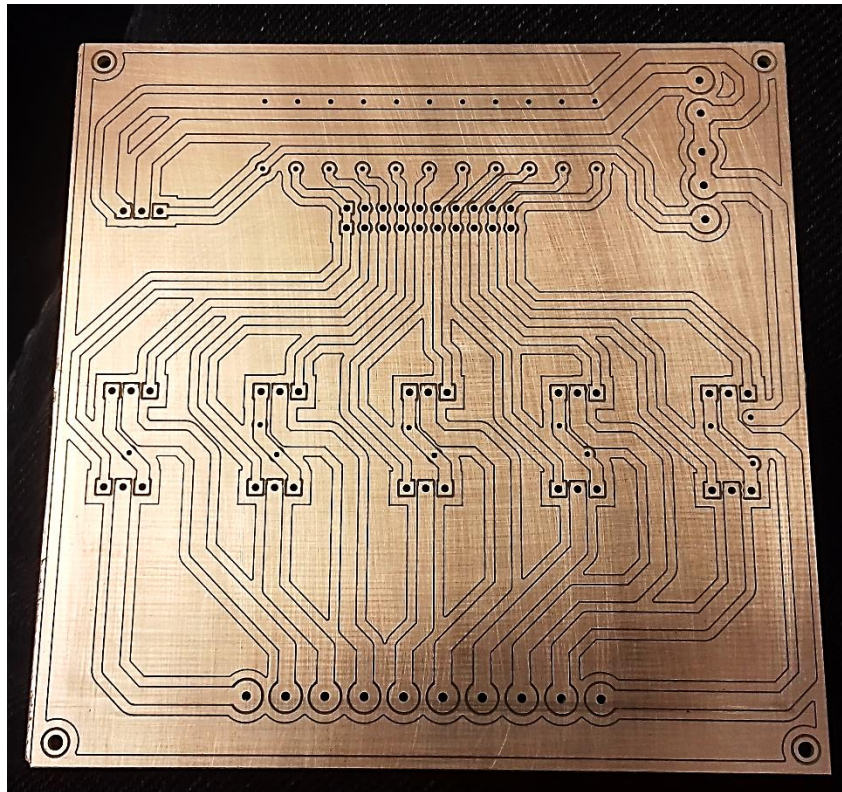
Placa de circuito impreso maquinada en CNC
